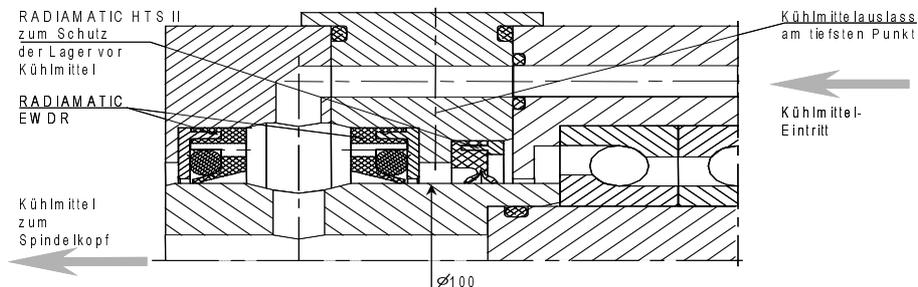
RADIAMATIC EWDR in der Drehdurchführung einer Werkzeugmaschinen­spindel (1,4 MPa, 3000 1/min)
